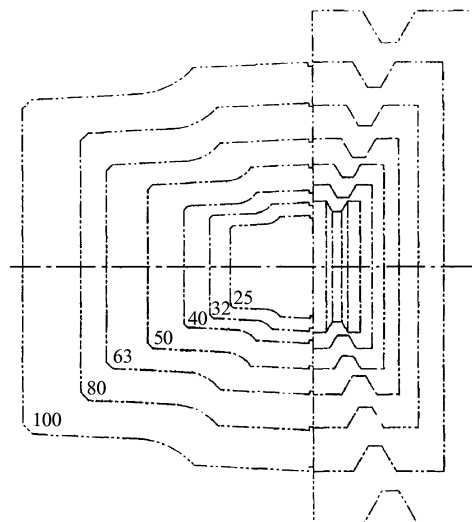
Типоразмеры хвостовиков инструмента унифицированных конструкций
